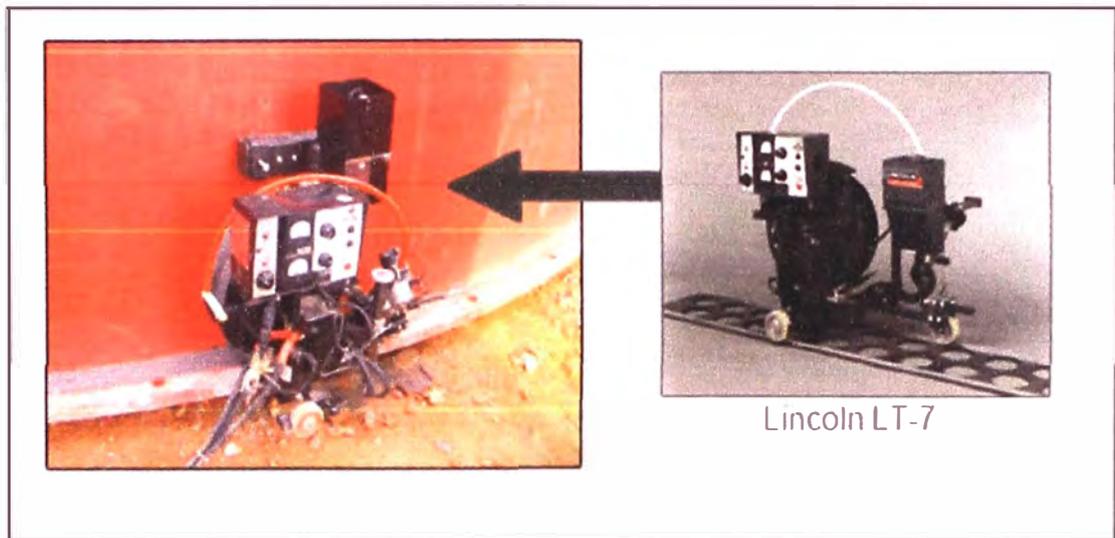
Welding tractor, Marca Lincoln
